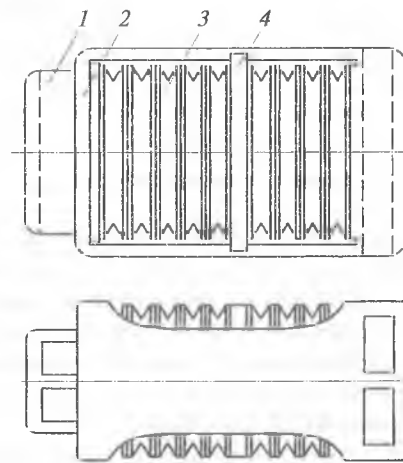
Поглощающий аппарат пассажирских локомотивов и вагонов: 1 — нажимной конус; 2 — направляющий корпус; 3 — резинометаллический элемент; 4 — планка
